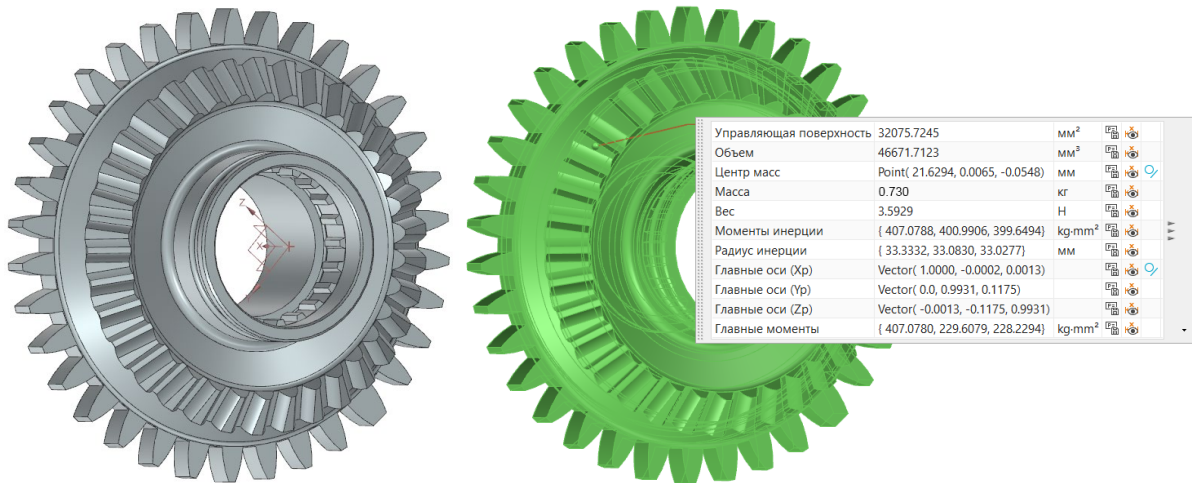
Тривимірне зображення деталі – шестерня конічна
